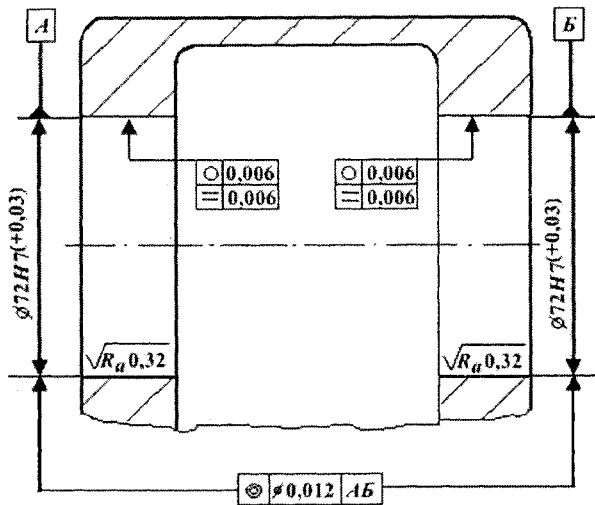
Пример обозначения точностных требований к поверхностям отверстий корпуса, сопрягаемым с подшипником качения
